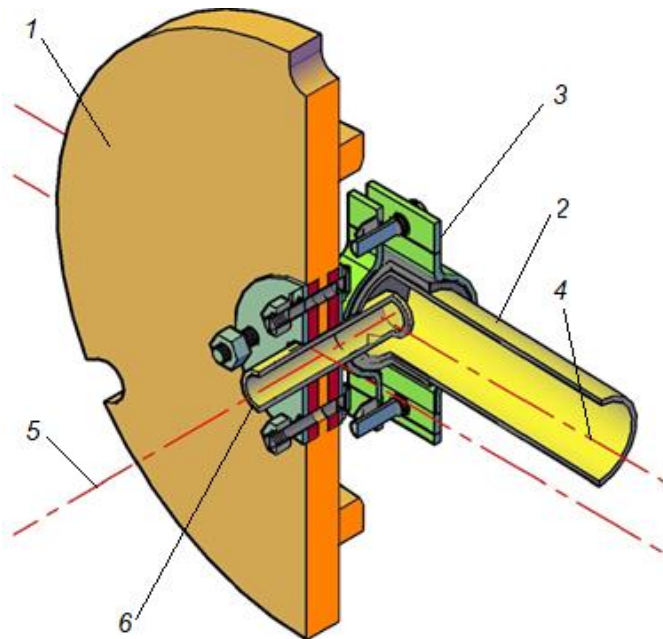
Розріз вузла кріплення фрагмента РТ з досліджуваною насадкою: 1 – кришка передньої основи напірного бака; 2 – відрізок розподільного трубопроводу; 3 – елементи кріплення РТ; 4 – вісь РТ; 5 – вісь насадки; 6 – торцевий вихідний отвір насадки
